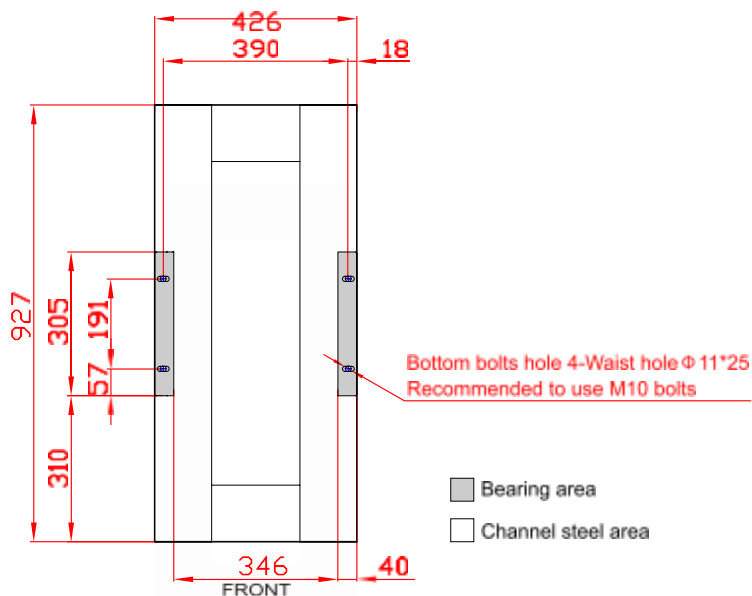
Рекомендуемый установочный размер швеллера .
